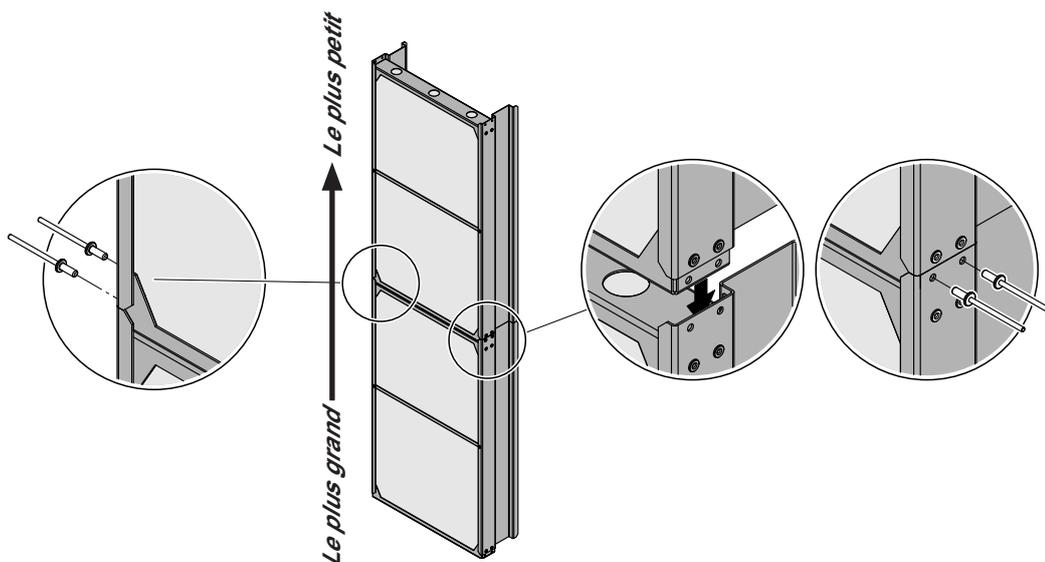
Rivetage des bancs des cassettes de séparateur de gouttelettes ensemble
